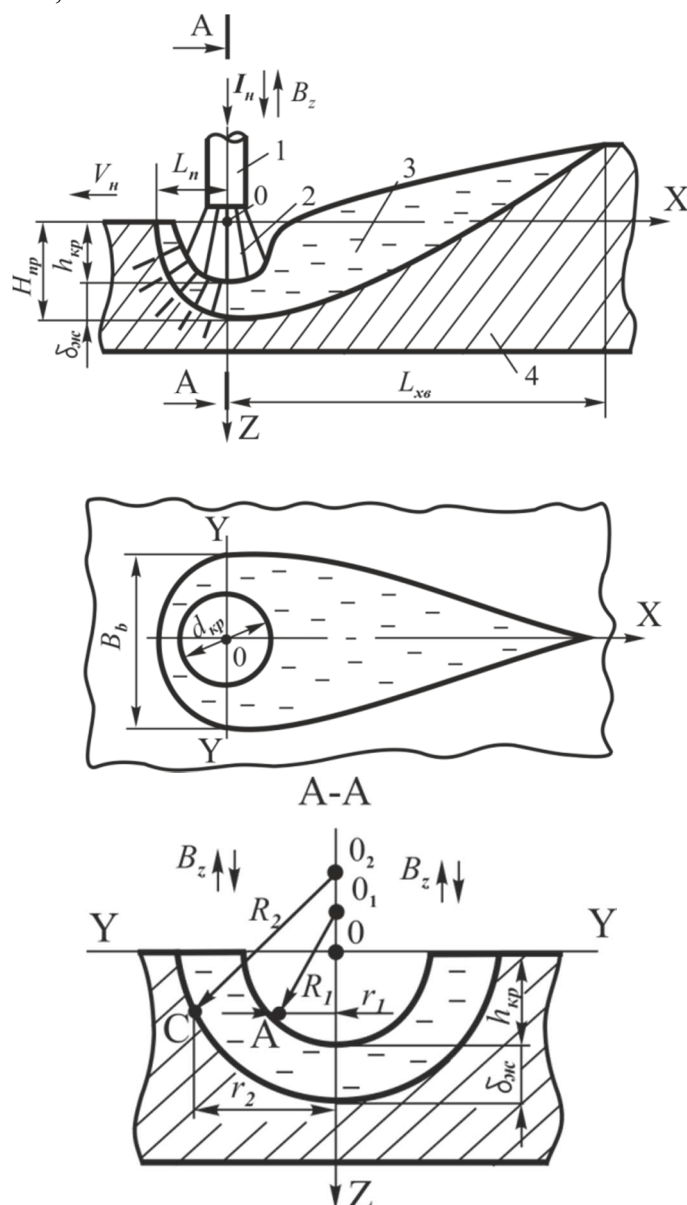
Схема сварочной ванны при дуговой наплавке и ее геометрические размеры:
